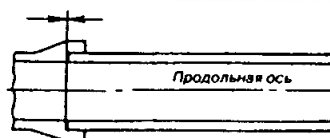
Качественное соединение при помощи раструбной или раструбно-стыковой сварки (деталь плотно облегает поверхность трубы, поверхность гладкая без зазоров)
